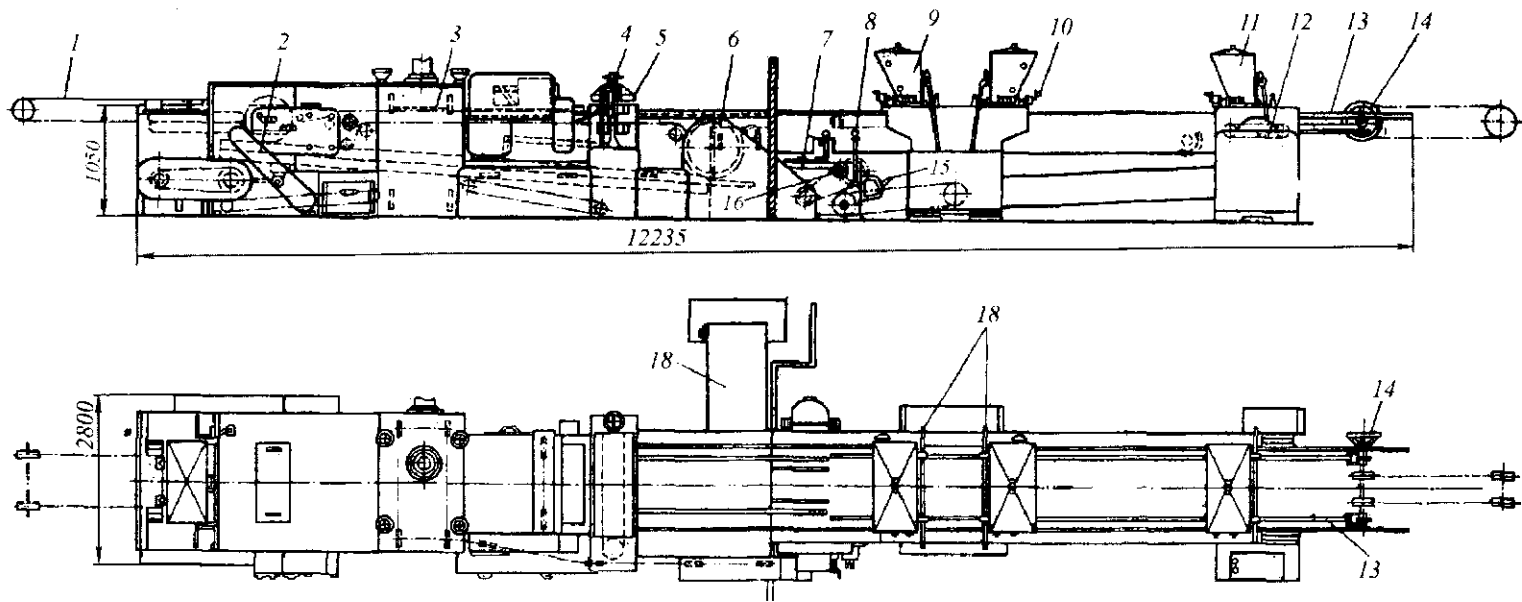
Конфетоотливочный агрегат с порядным заполнением форм
